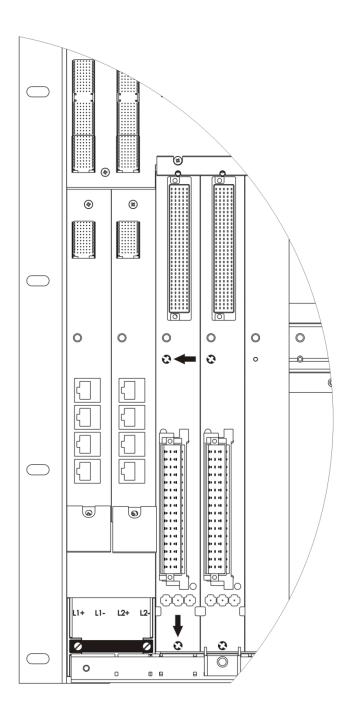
Festschrauben des Mono Connector Boards, exemplarisch
